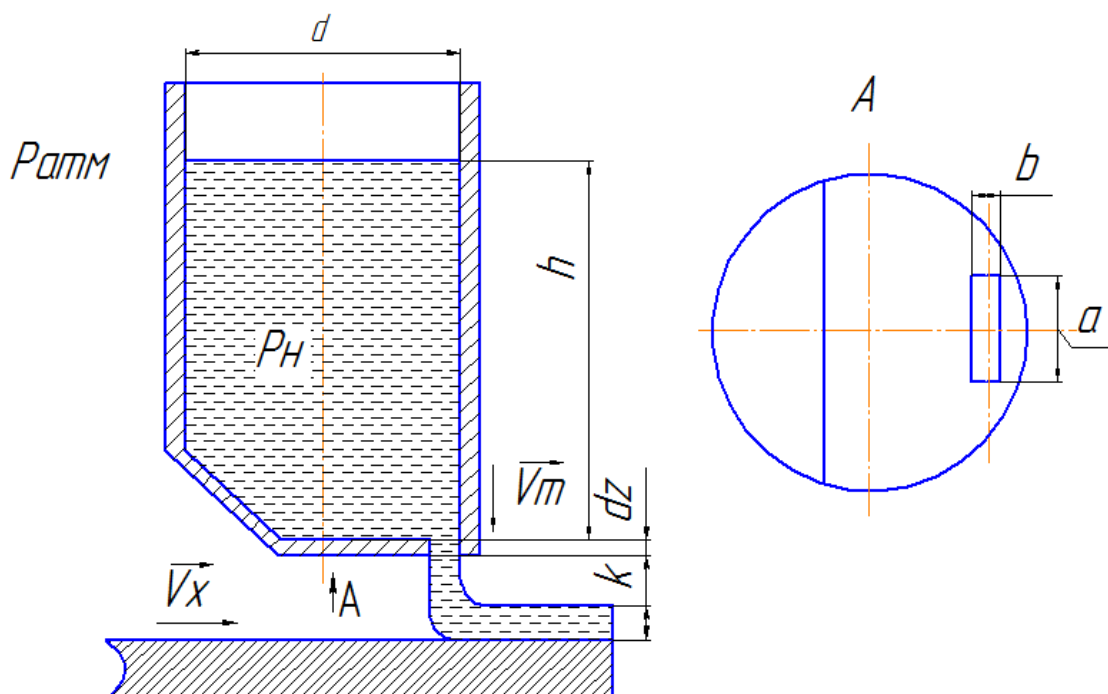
Схема подачі розплаву на поверхню основи для виготовлення біметалу
